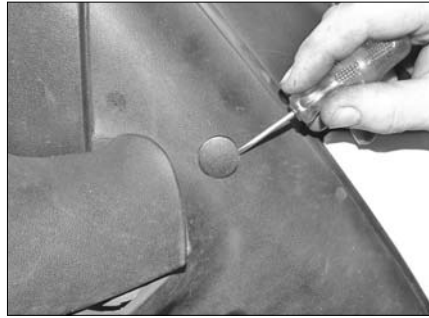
Снимите декоративные крышки над болтами крепления основания зеркала
